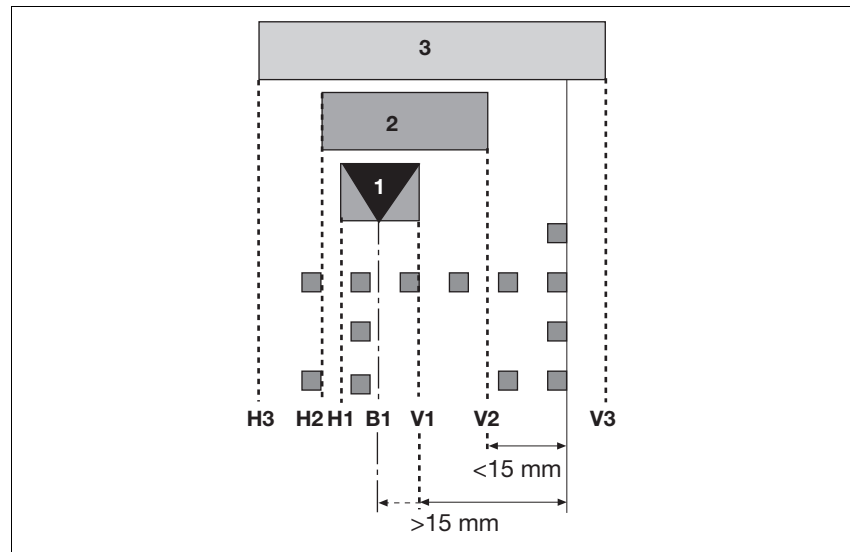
Einteilung der Werkzeuge in Werkzeugklassen
